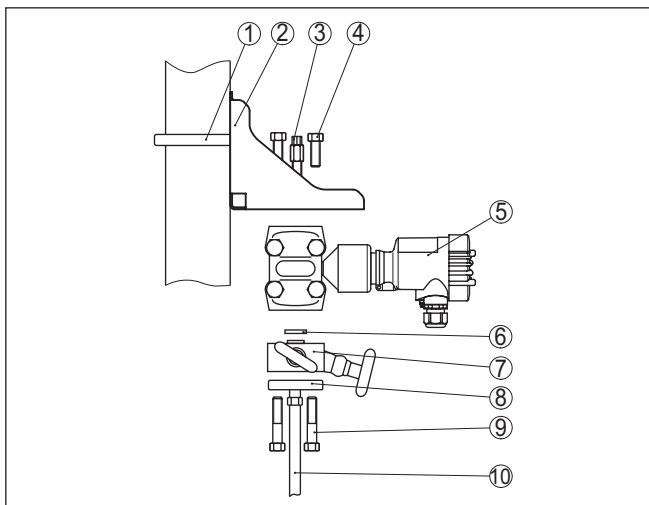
Disposizione di montaggio in caso di montaggio su tubo
